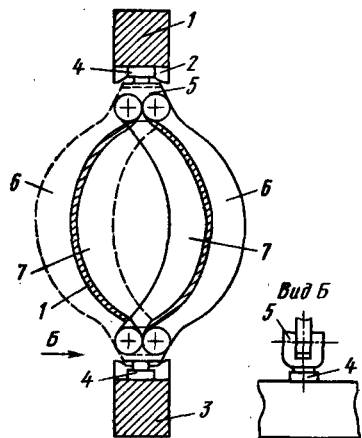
Приспособление для групповой сборки панелей с симметричными обводами
